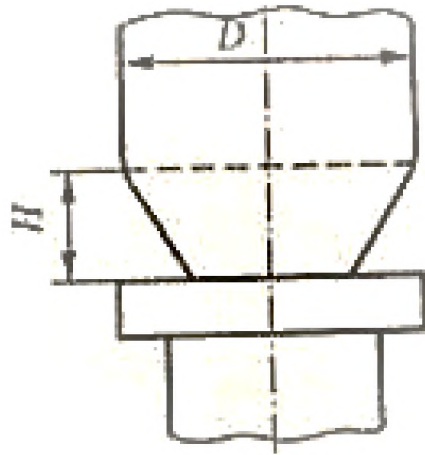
Форма рукава в зоні роздування плівки
